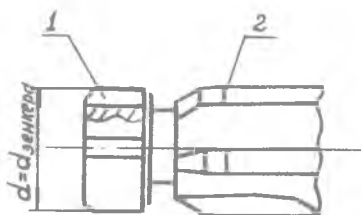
Развертка с направляющими, расположенными перед режущими зубьями:
